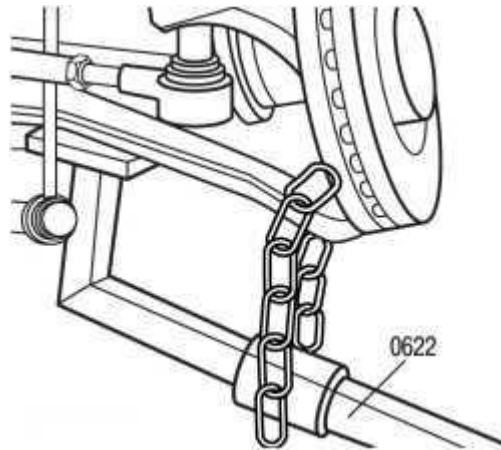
Застосування важеля «0622» для роз'єднання кульових опор з поворотною цапфою
